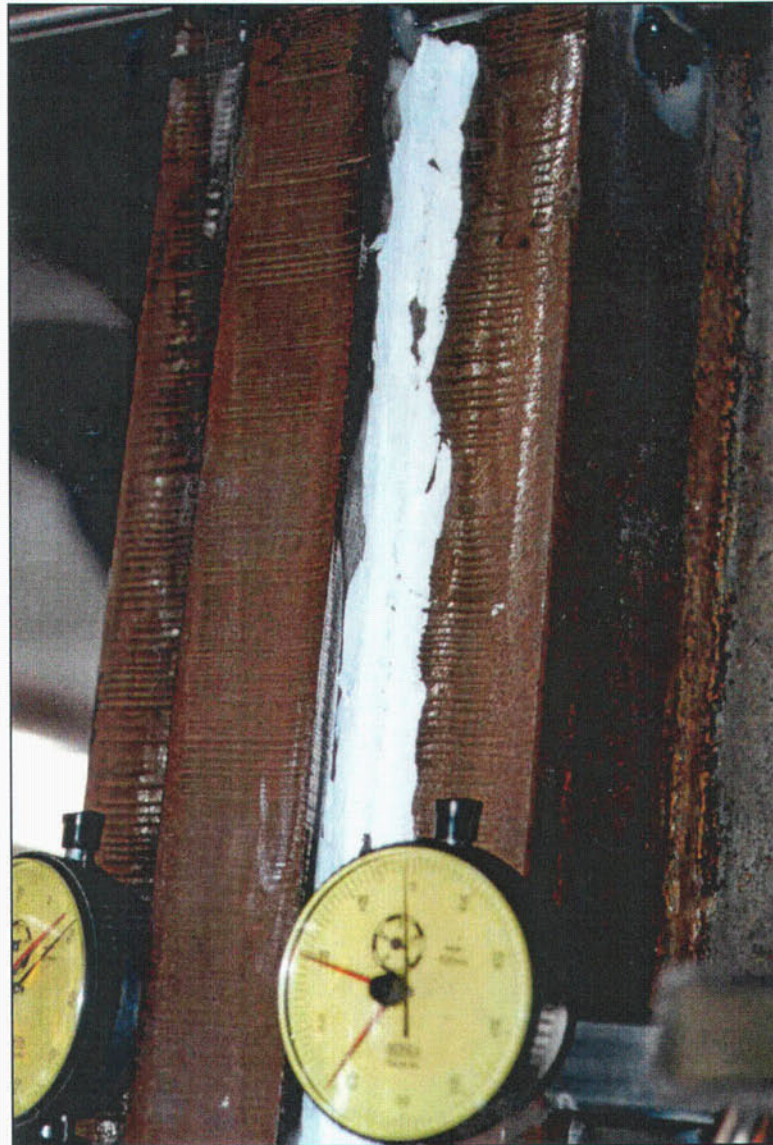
Probeta 3M. La fotografía se ha tomado durante el ensayo de rotura. Se observa la cal agrietada en toda la longitud de la soldadura (30 cm.), señal de que dicha soldadura se encuentra prácticamente plastificada.
